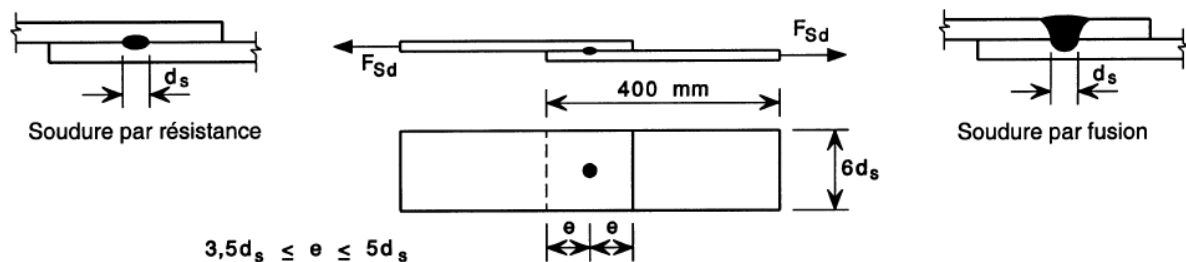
Éprouvettes pour essais de cisaillement sur soudures par points
